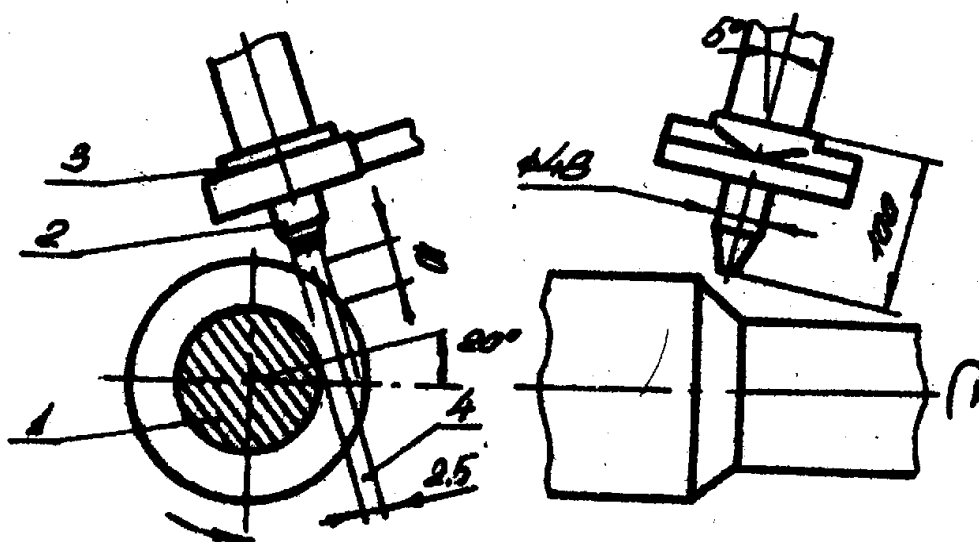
Відносне розташування плазмового пальника до оброблюваної деталі.
